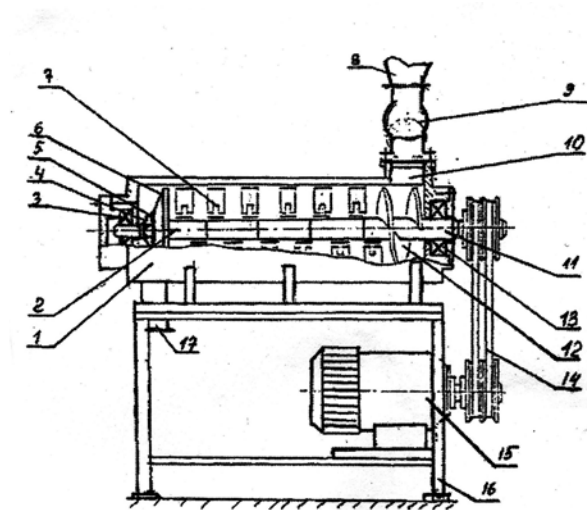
Конструкция скоростного гранулятора: 1 – корпус; 2 – втулка; 3 – подшипник; 4 – гайка; 5 – стопорная шайба; 6 – отбойный диск; 7 – плоская лопатка; 8 – загрузочный бункер; 9 – секторный питатель; 10 – загрузочный патрубок; 11 – рабочий вал; 12 – транспортирующий шнек; 13 – подшипник; 14 – клиноременная передача; 15 – электродвигатель; 16 – рама; 17 – патрубок выгрузки.
